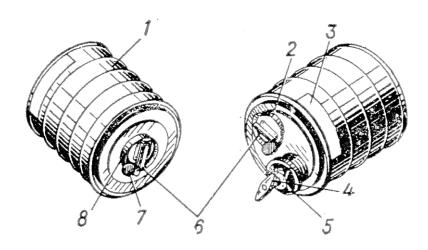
Регенеративный патрон РП-4: 1 — корпус; 2 — гнездо ниппеля для присоединения лицевой части; 3 — полоса термоиндикаторной краски; 4 — пусковое устройство винтового типа; 5 — чека; 6 — заглушки; 7 — пломба; 8 — гнездо ниппеля для присоединения дыхательного мешка
